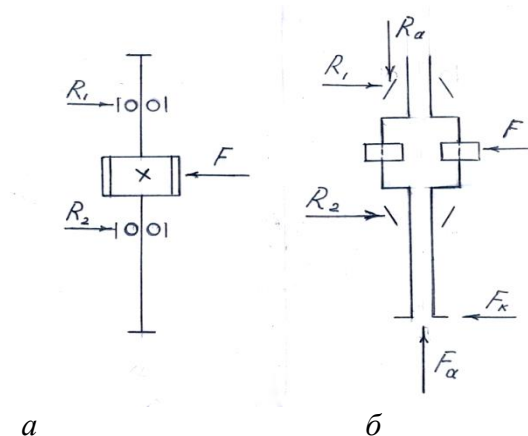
Розрахункові схеми для підшипників: а – центрального вала шестерні; б – сателітів та води́ла з полим вихідним валом.
